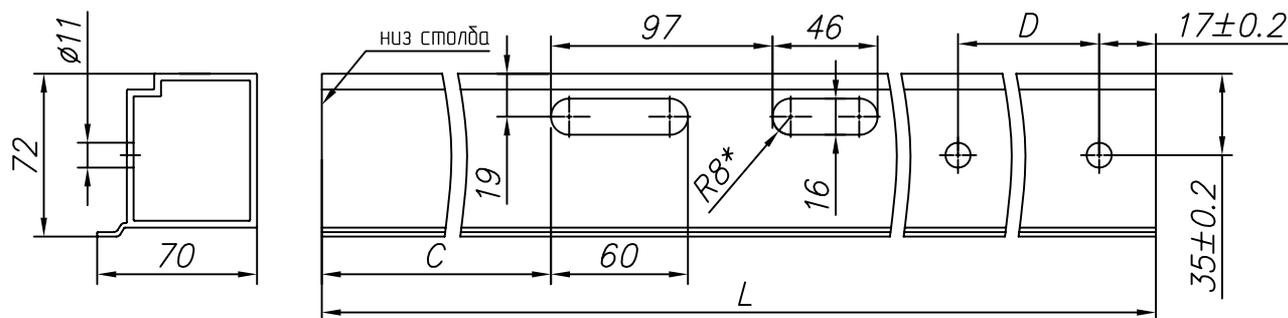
Изготовление столба притвора с пазом для ответной пластины замка для калитки с правым открыванием
